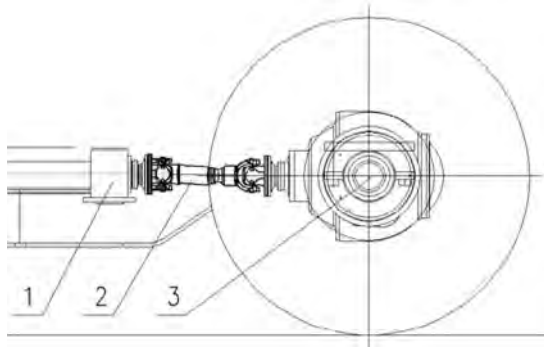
Схема установки двухшарнирной карданной передачи на машине: 1 – опора; 2 – карданный вал; 3 – задний мост с колесами
